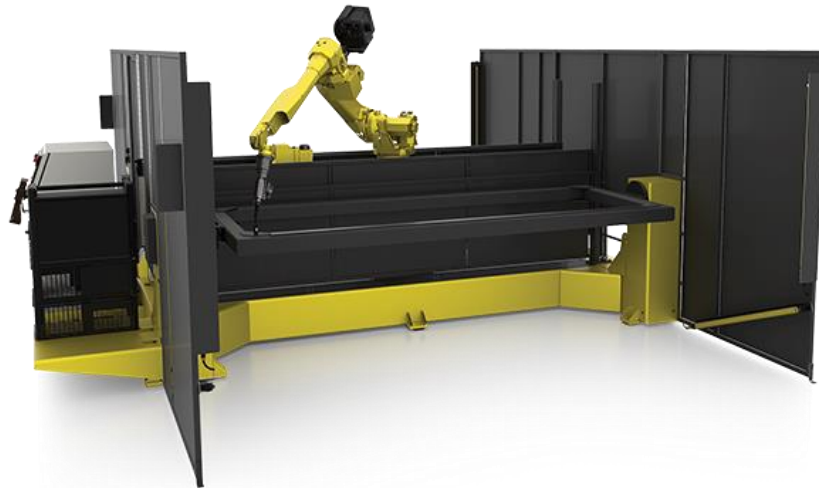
Célula de soldadura robotizada FANUC incluída na proposta da Motofil S.A. [31]
